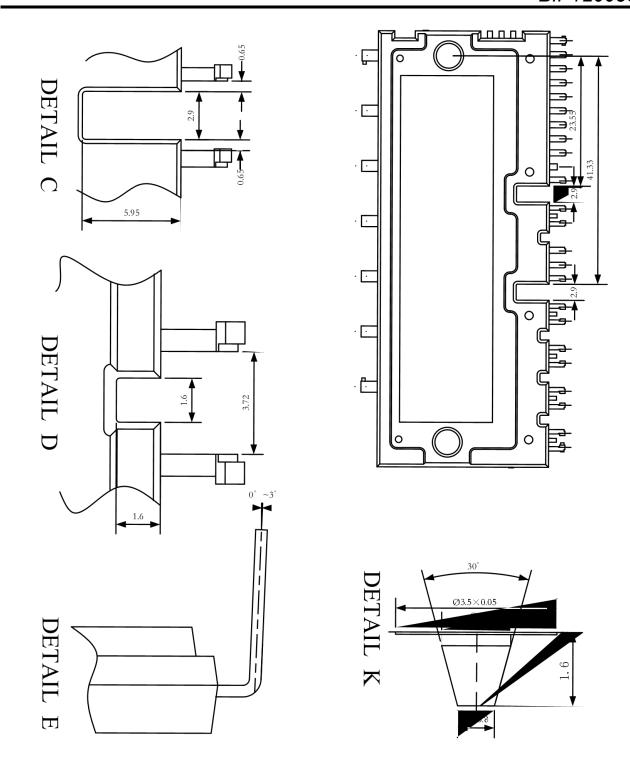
封装轮廓详图 Fig 9. Package Outline Drawings
